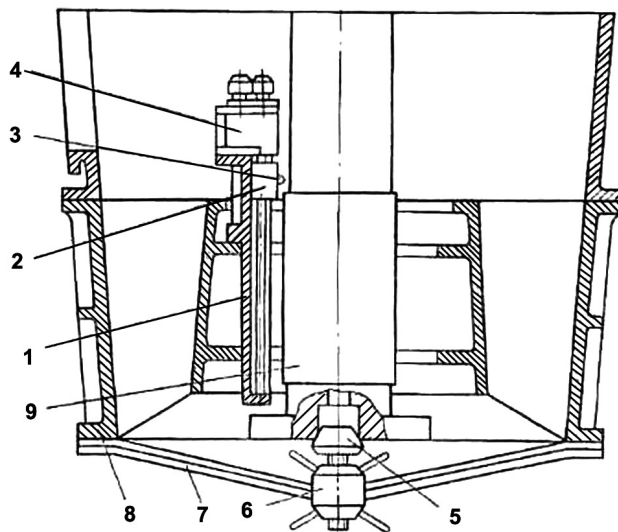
Схема устройства для обточки шеек вала насоса типа ОПВ-260ЭГ:
